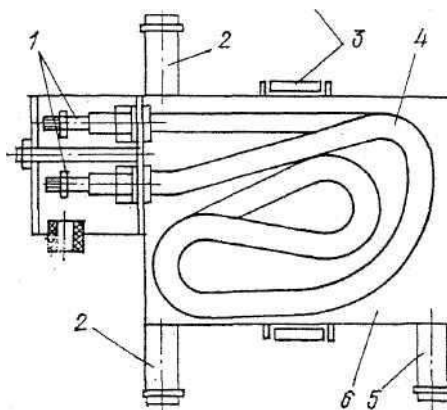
Контактный электронагреватель конструкции НИИАТ: 1 – контактные выводы; 2 – входные патрубки; 3 – хомут крепления; 4 – ТЭН; 5 – выходной патрубок; 6 – корпус теплообменника.
